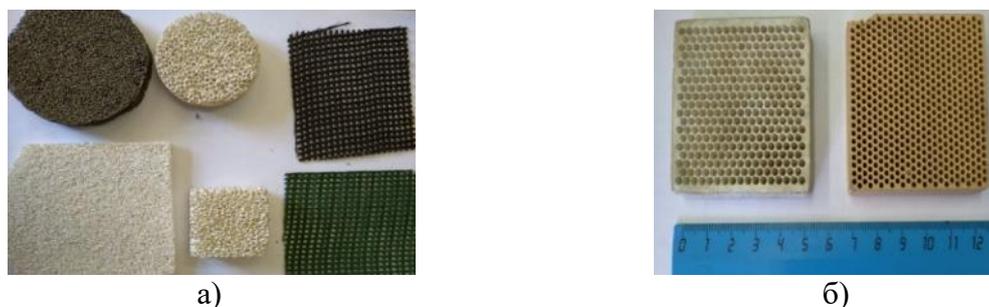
Внешний вид фильтрующих элементов: а – сетчатые и пенокерамические; б – прессованные керамические
